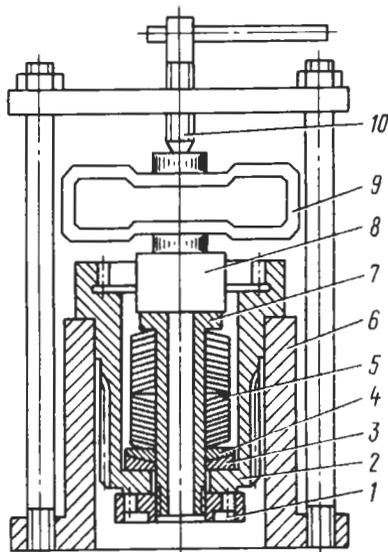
Сборочный узел для предварительного нагружения пакета тарельчатых пружин
